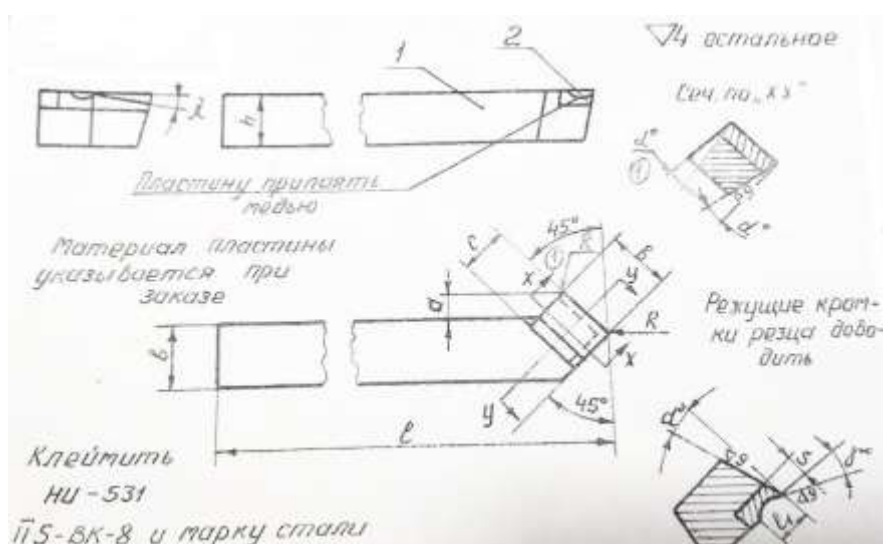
Чертеж проходного резца НИ 531-II-4
